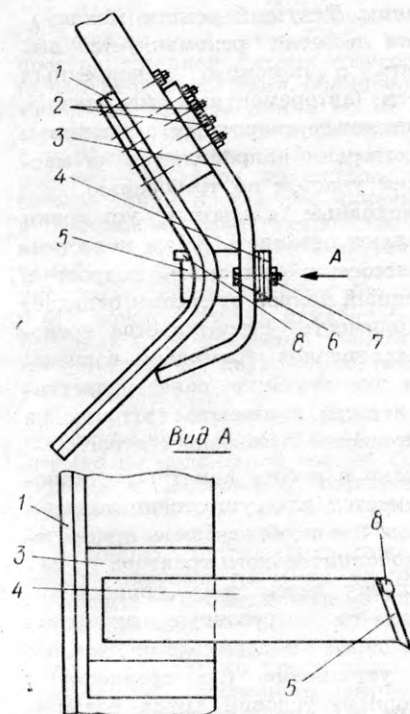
Схема установки дополнительного приспособления на машине ЛП-30Б:
